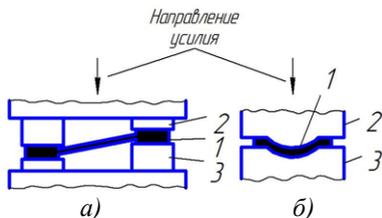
Схемы калибровки: а – плоскостная; б – объемная; 1 – поковка; 2, 3 – элементы штампа
